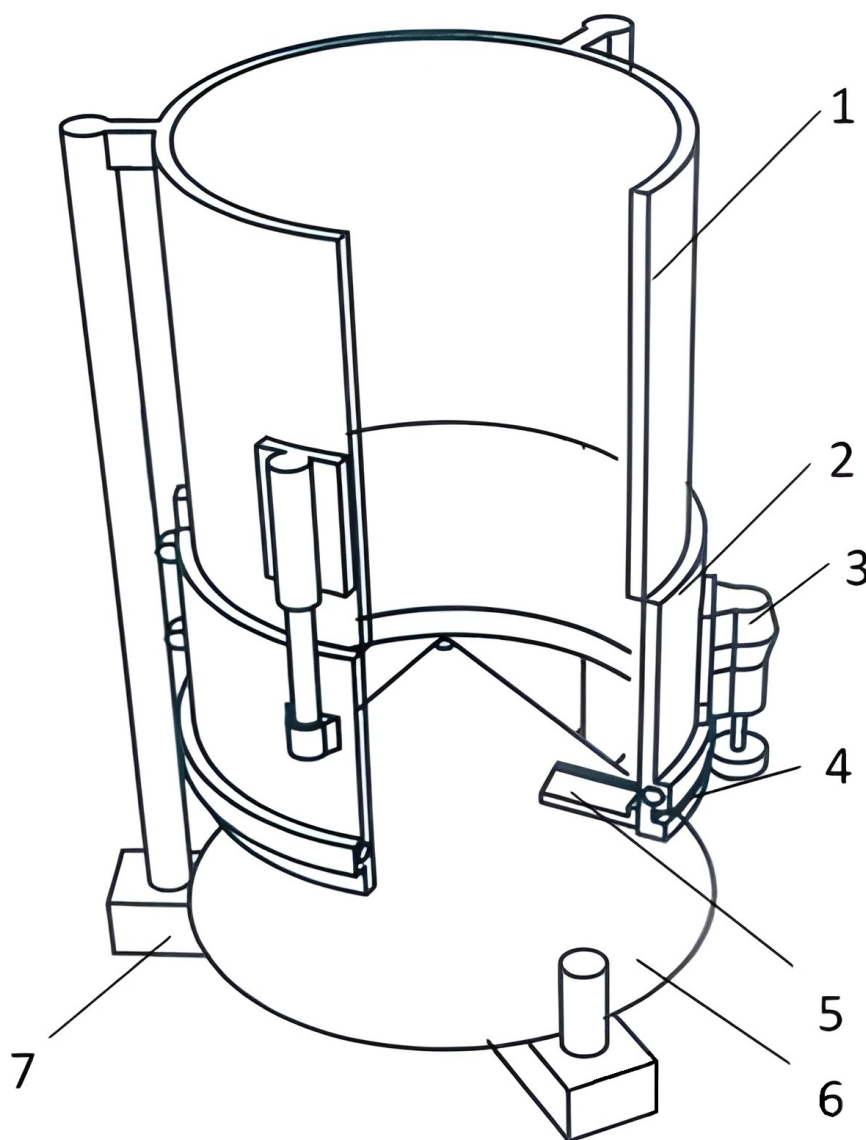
Схема бункера с рыхлителем на кольцевом затворе
